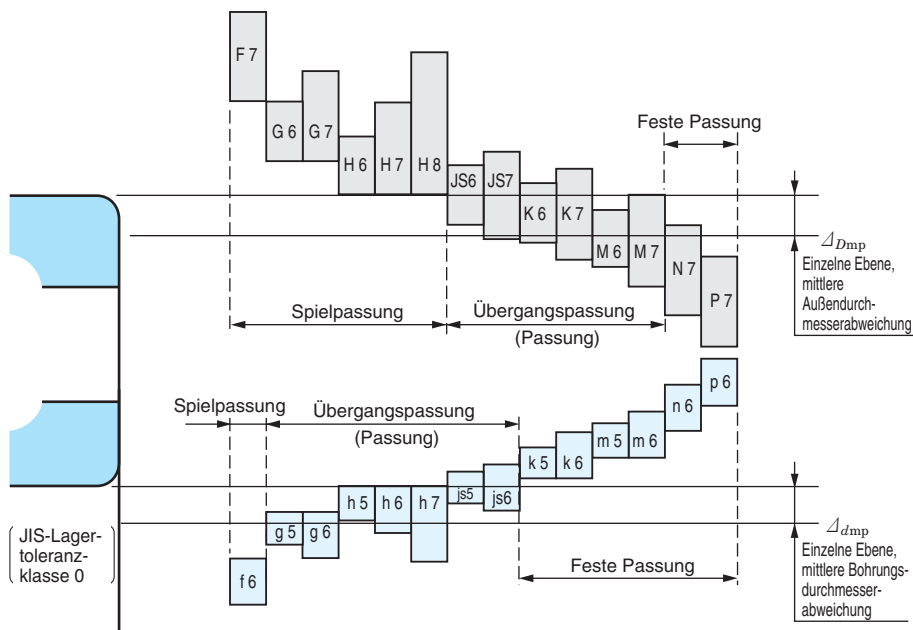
Zusammenhang zwischen Toleranzen für Wellen-/Gehäusebohrungsdurchmesser und Passungen
